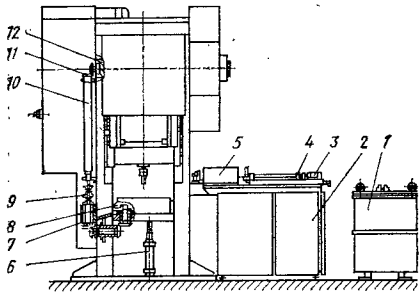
Общий вид прессы и установки для нагрева заготовок:
